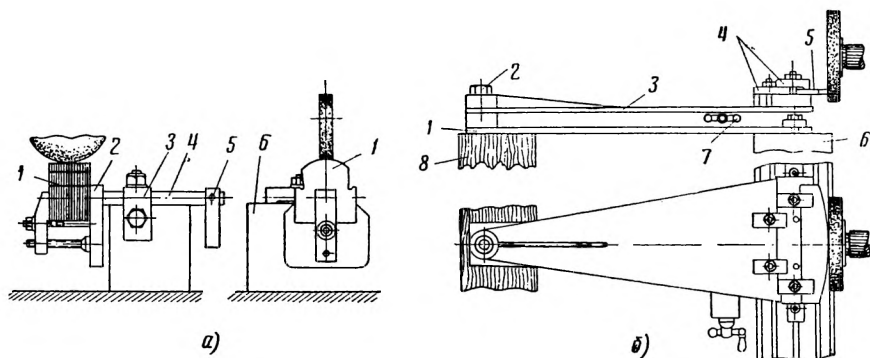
Приспособление для шлифования выпуклых цилиндрических поверхностей:
